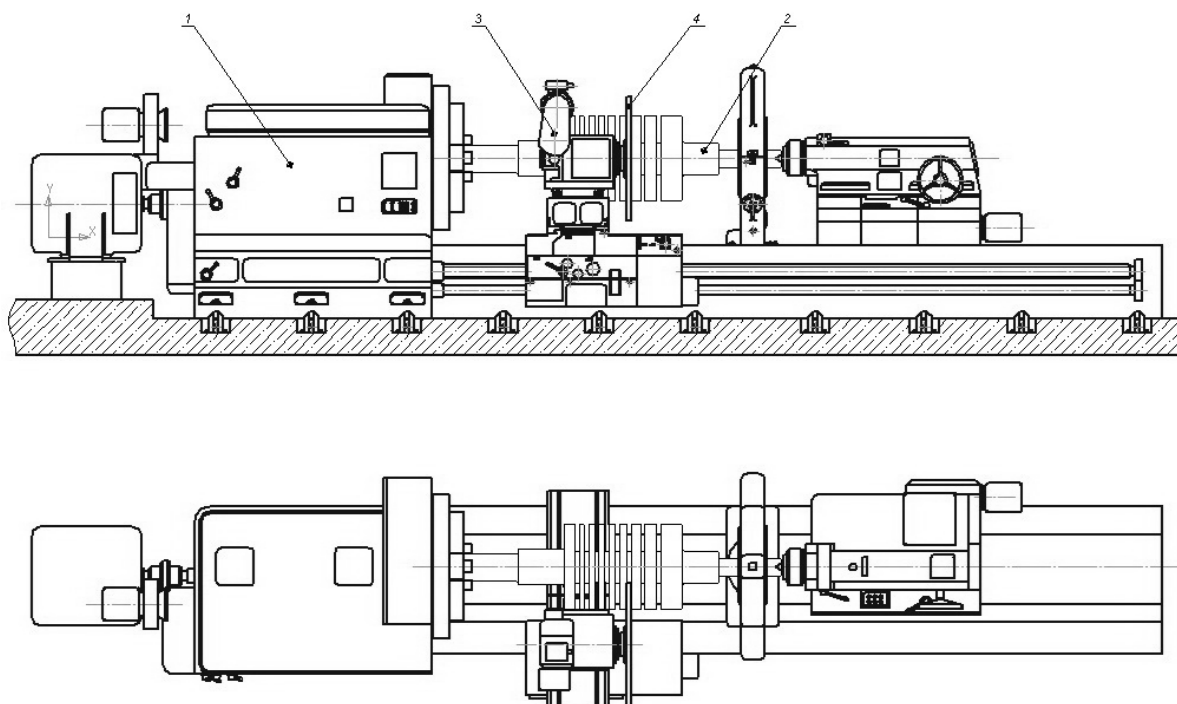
Схема модернизации станка модели КЖ16119Ф2 под фрезерование глубоких пазов ротора турбины (вид сверху).
